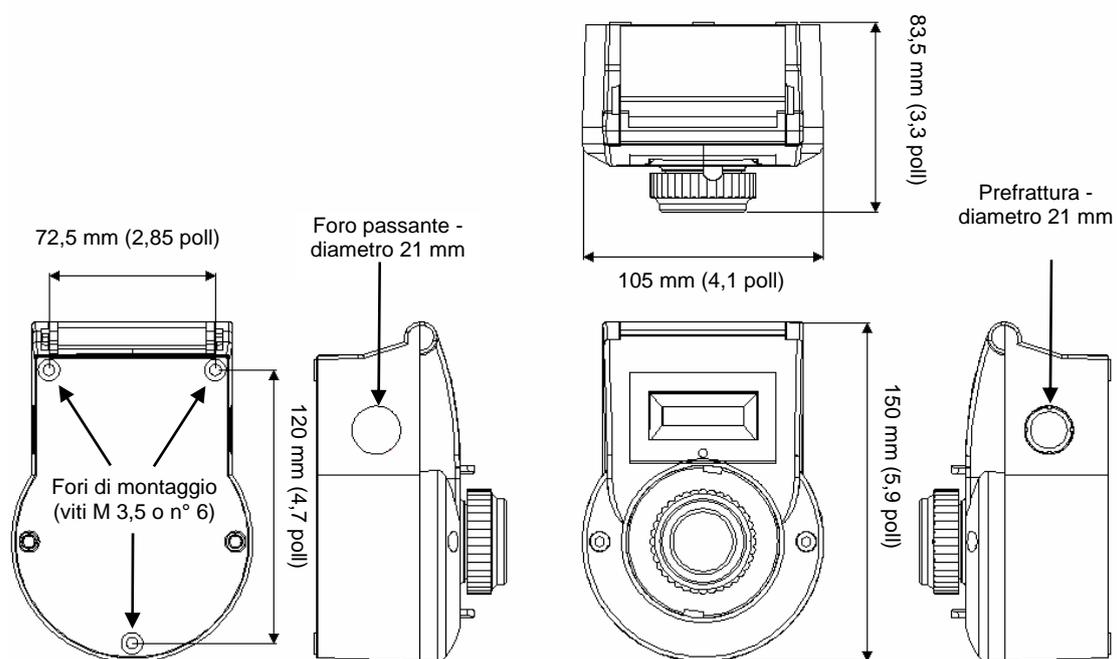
dimensioni del rivelatore e posizioni dei fori di montaggio
